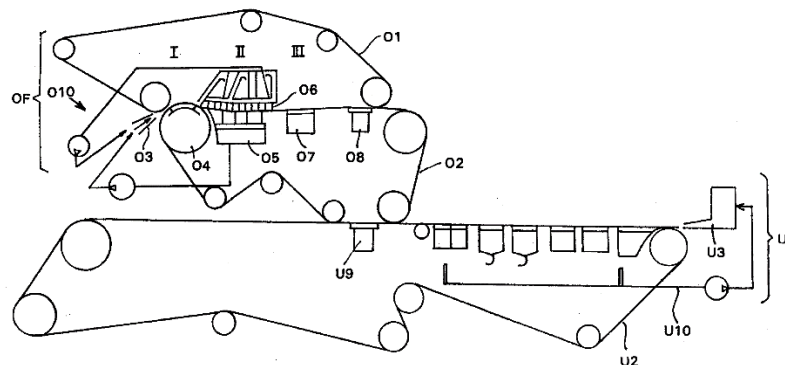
Двосіткова формуюча частина для виготовлення багатошарового паперового полотна
